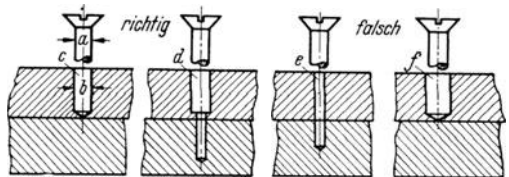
Vorbohren von Schraubenlöchern in Holz. *a* = Halsdurchmesser der Schraube; *b* = Bohrlochdurchmesser.
